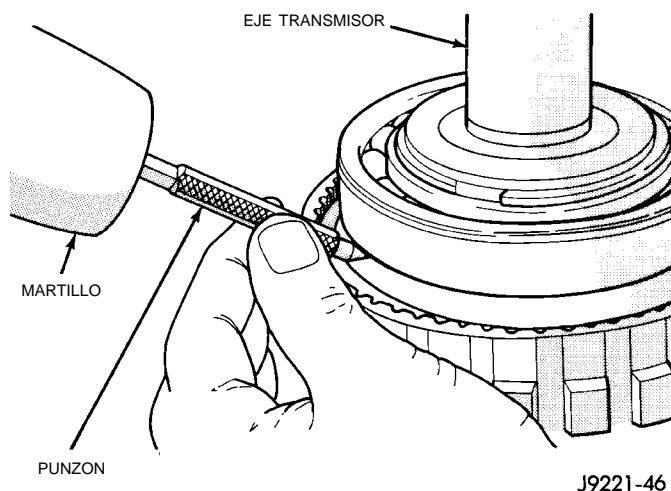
Marcas del engranaje anular y el eje transmisor para la alineación durante el ensamblaje
